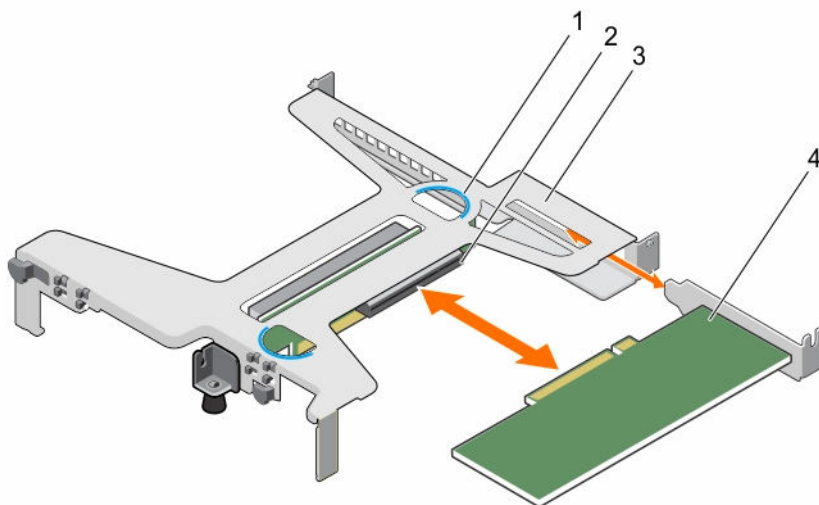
Remover e instalar a placa de expansão na riser da placa de expansão
